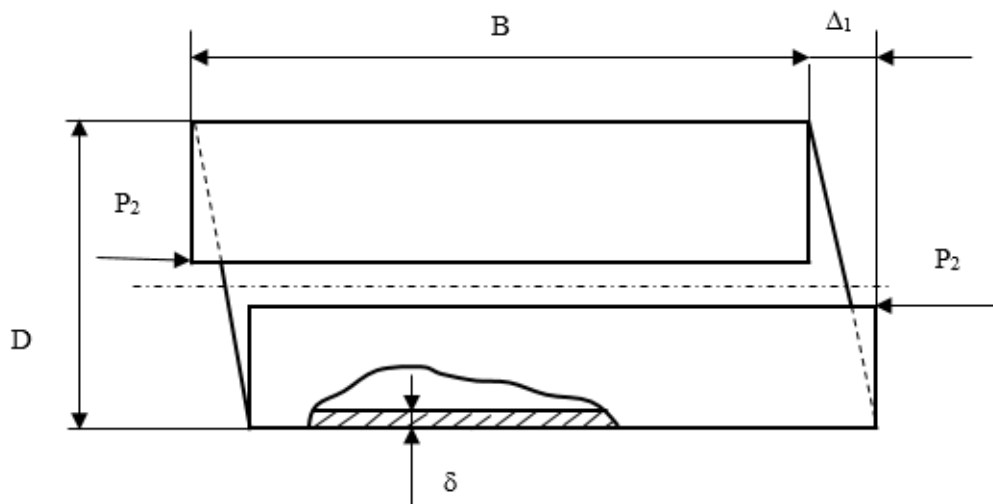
Розрахункова схема визначення величини сили для вирівнювання торців циліндричної обичайки
